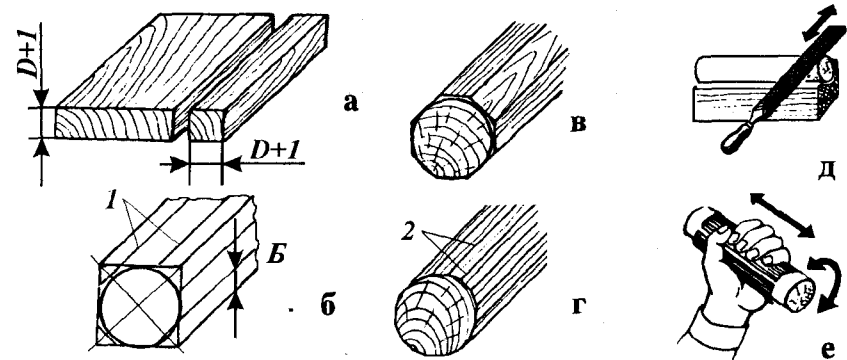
Последовательность изготовления детали цилиндрической формы ручным инструментом: а — выпиливание бруска квадратного сечения из доски; б — разметка торцов и граней заготовки; в — восьмигранная форма заготовки; г — шестнадцатигранная форма заготовки; д — обработка круглой формы напильником; е — зачистка шлифовальной шкуркой
